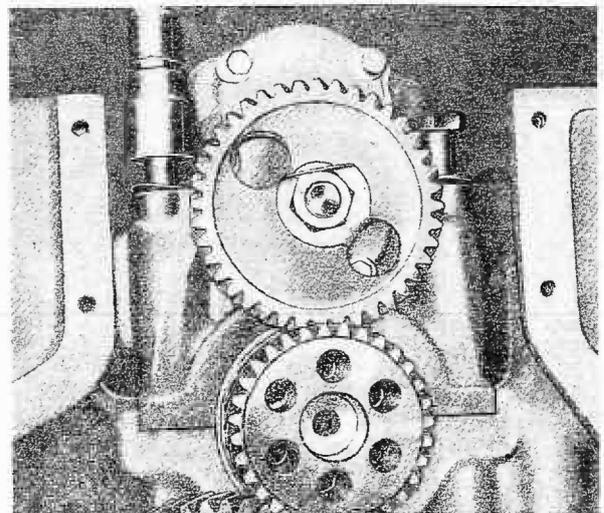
Lagerdeckel 7 [4] mit Ölpumpe abschrauben
